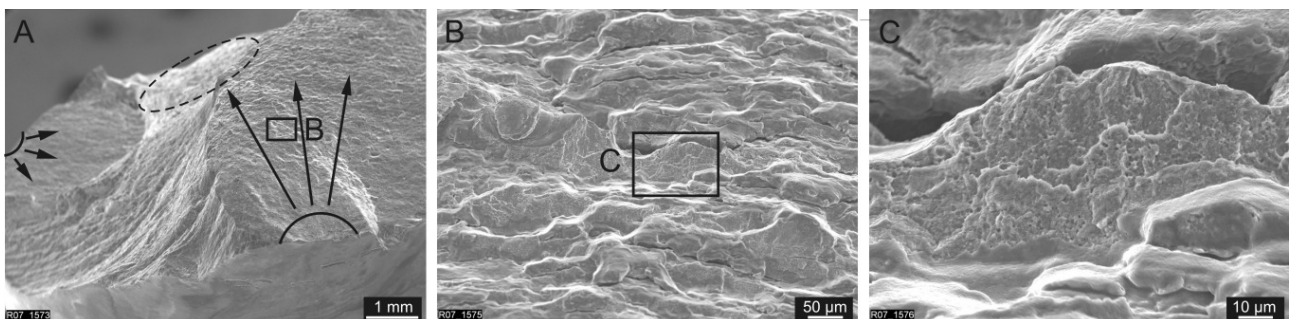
Rissausgang Ausschnitt B aus Bruchfläche Detail C, Mikroduktilität
